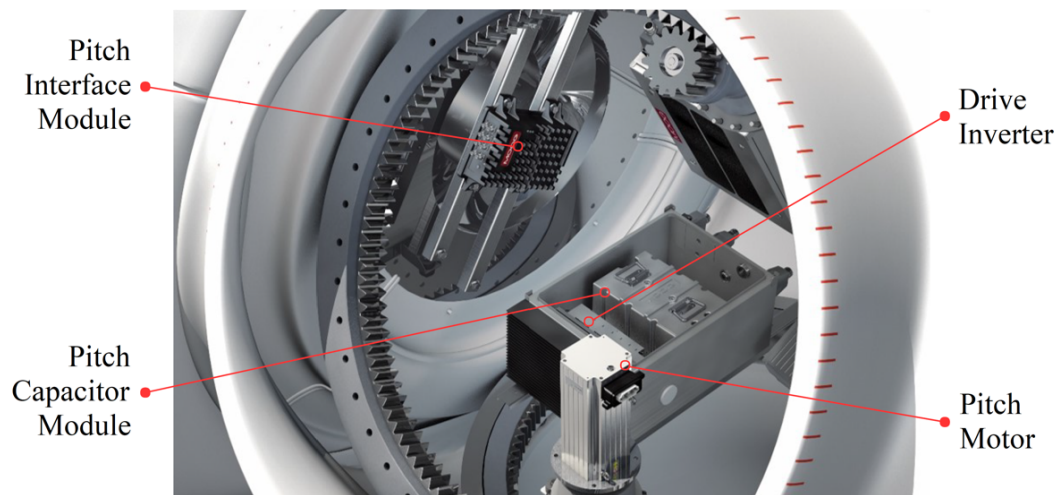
Rotornabe mit den Teilkomponenten [5]
